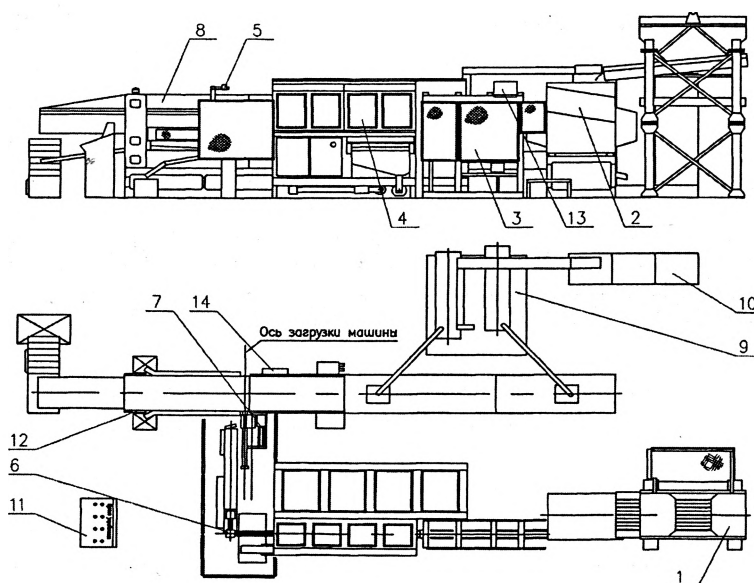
Общий вид линии поперечно-клиновой прокатки WRL63
